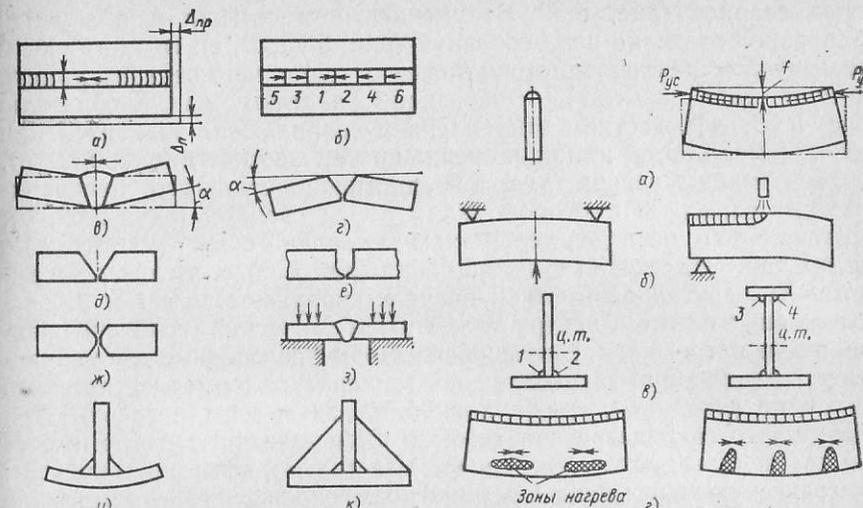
Усадка и угловая деформация сварных заготовок и способы их устранения:
